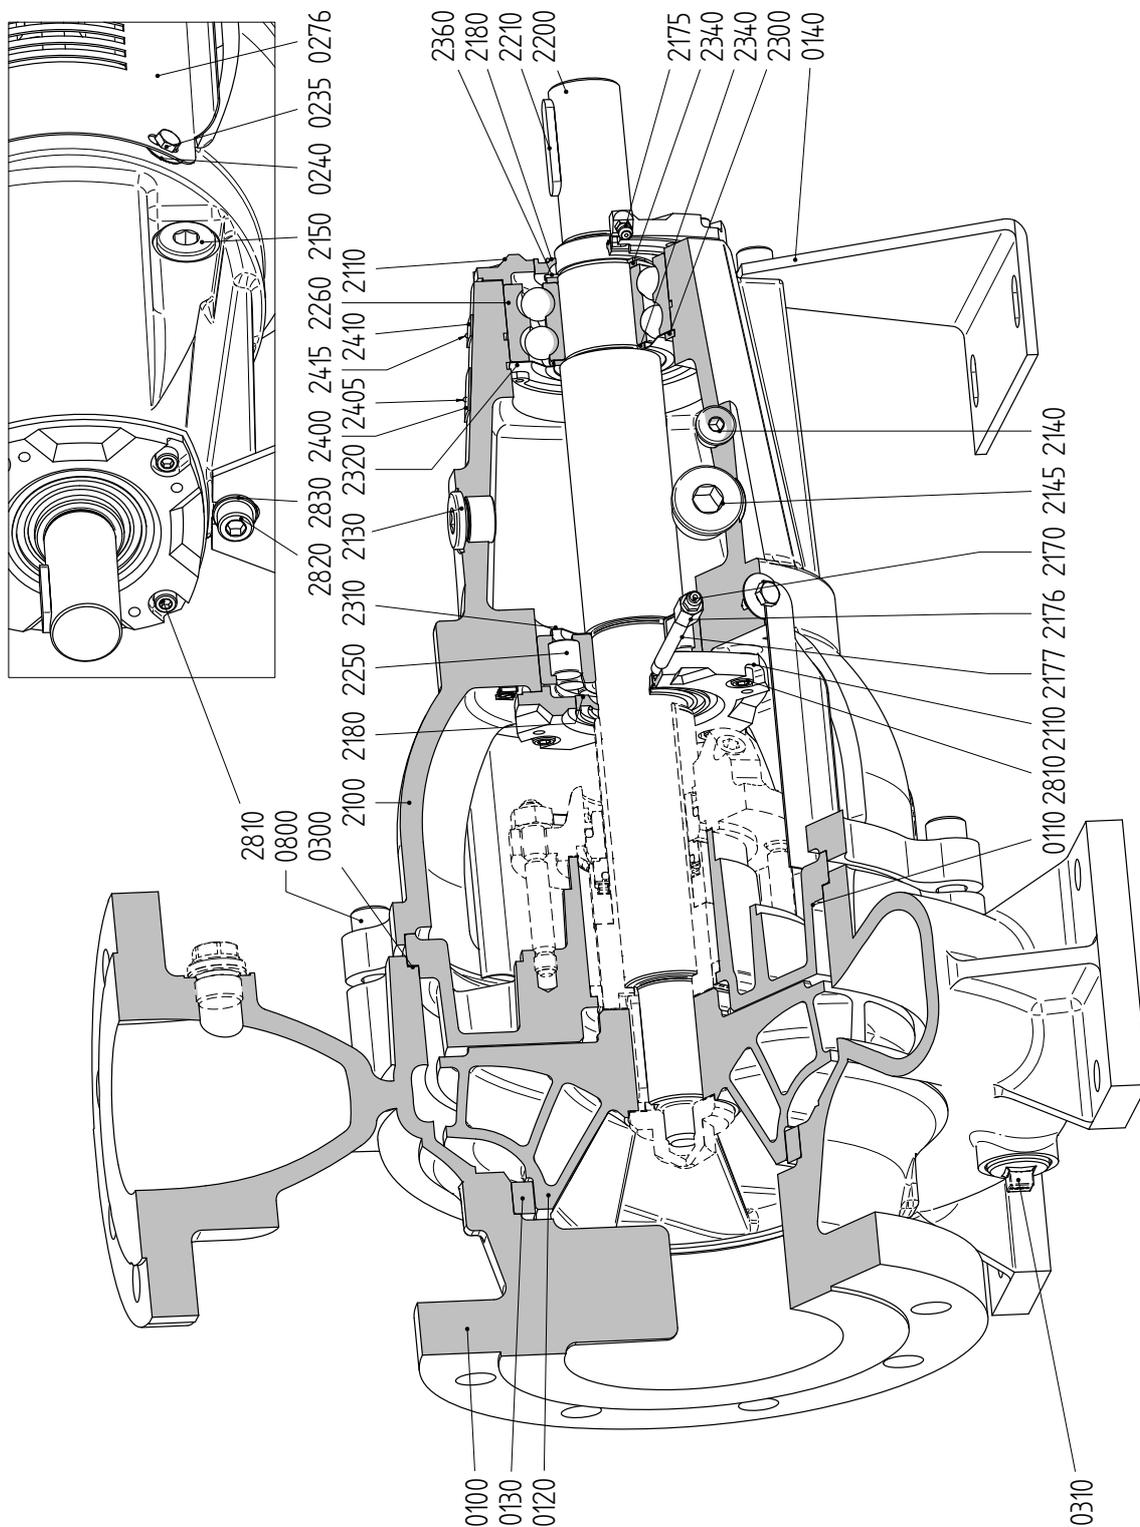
Schéma en coupe L2 - groupes de palier 1, 2, 3.
